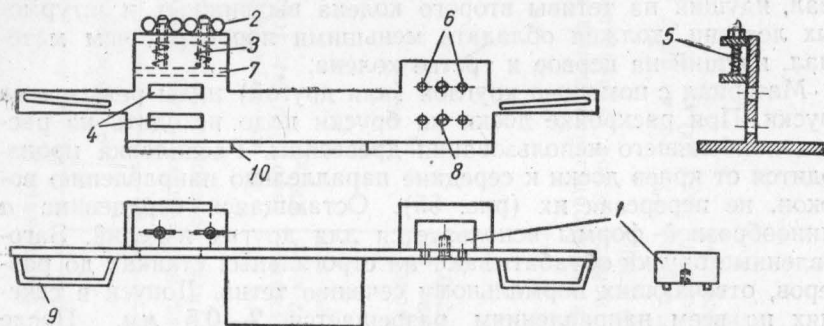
Кондуктор Мочалова для разметки гнезд:
